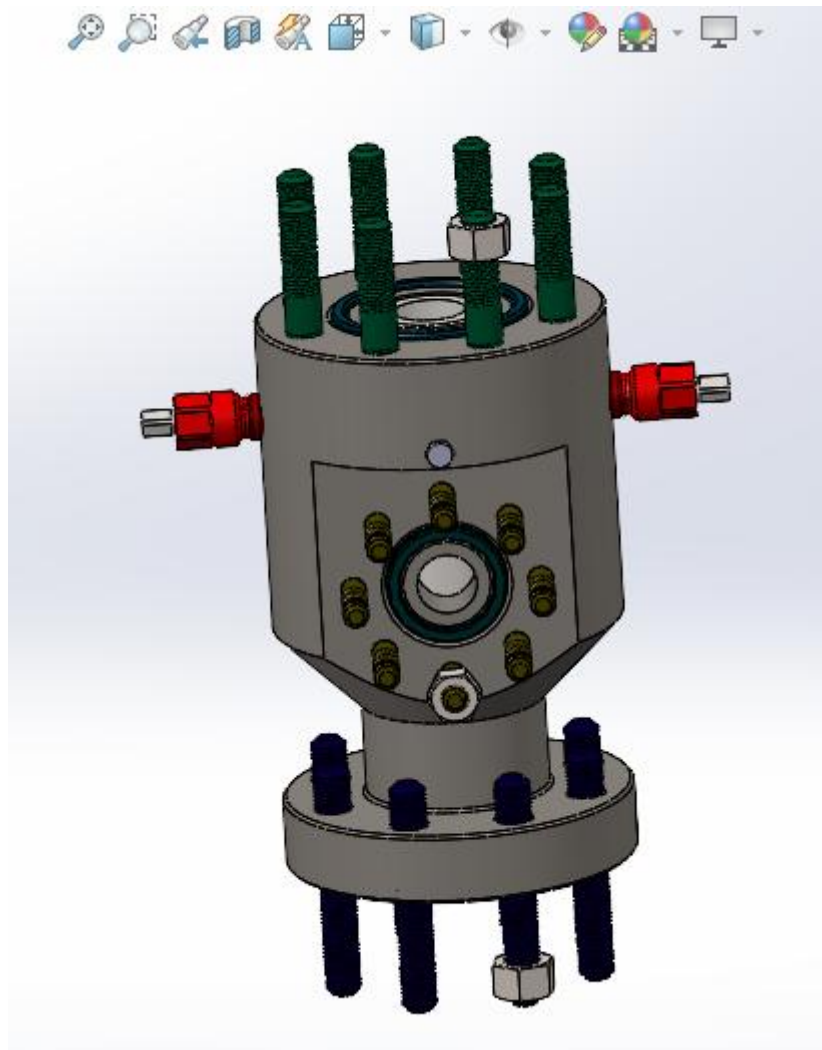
Tubing Head assemblée sur SolidWorks
